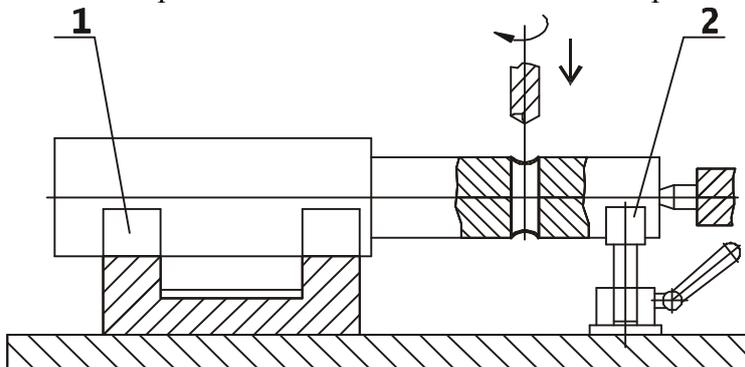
Схема базирования заготовки ориентируемой по двум внешним цилиндрическим поверхностям
